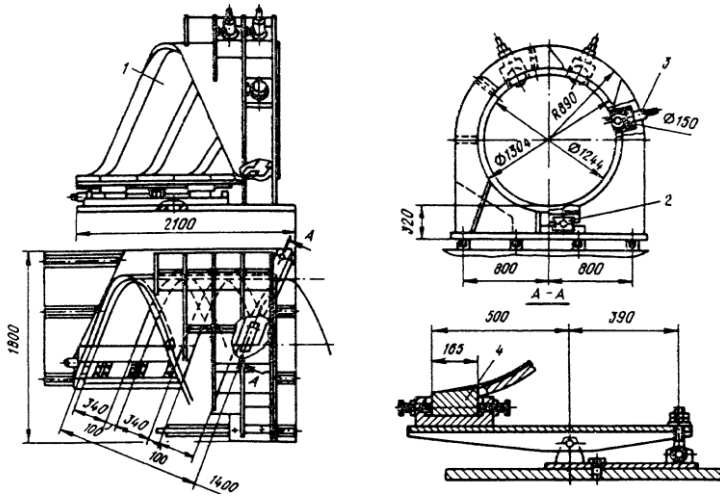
Формувальний пристрій напіввтулкового типу
